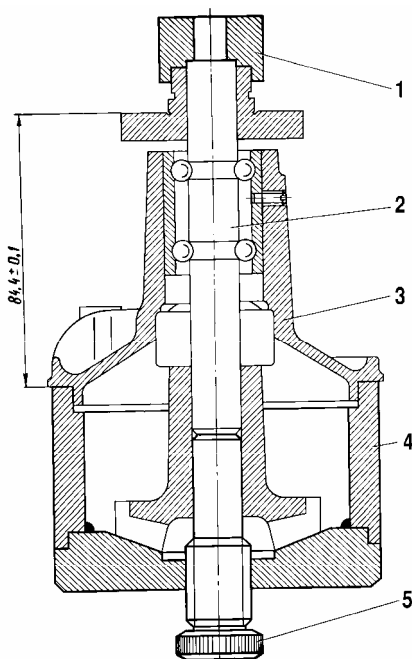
Напрессовка крыльчатки на валик насоса приспособлением А.60430:
